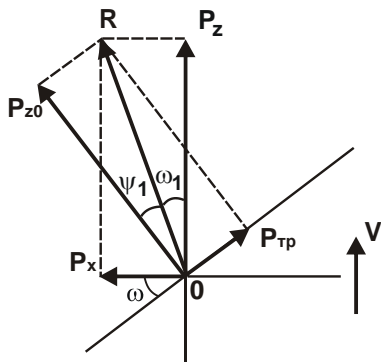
Розрахункова схема складових сили різання під час розвертання
